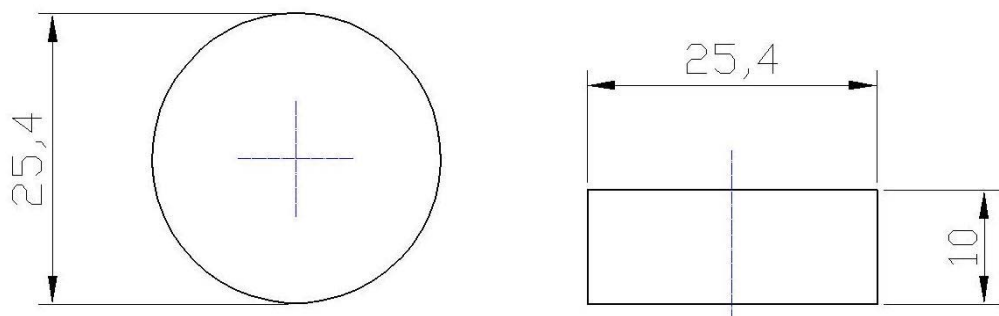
Dimensiones de las probetas de acero H13. (a) Vista superior. (b) Vista Lateral (Medidas en mm).
